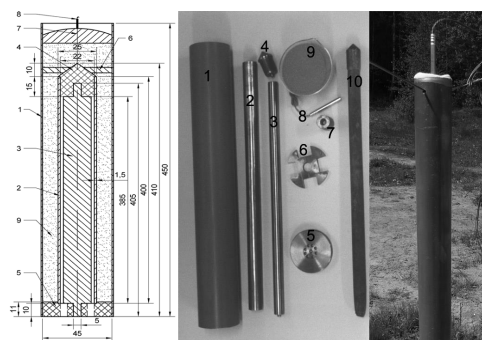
Система для соединения трубы и прутка путем взрыва: 1 – труба PVC; 2 – труба из меди; 3 – пруток из алюминия; 4 – верхняя центрирующая пробка; 5 – нижняя центрирующая пробка; 6 – верхний центрирующий кружок; 7 – детонатор; 8 – взрыватель; 9 – сыпучий материал взрывной; 10 – готовый биметаллический пруток Al-Cu.
